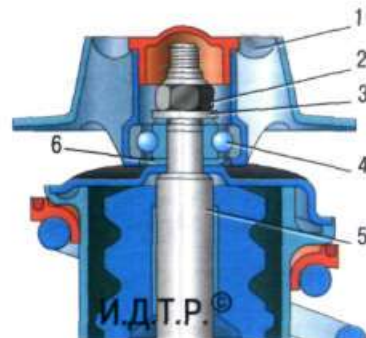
Подшипник верхней опоры телескопической стойки: 1 – верхняя опора; 2 – гайка; 3 – шайба; 4 – подшипник верхней опоры; 5 – шток амортизатора; 6 – тарельчатая шайба
